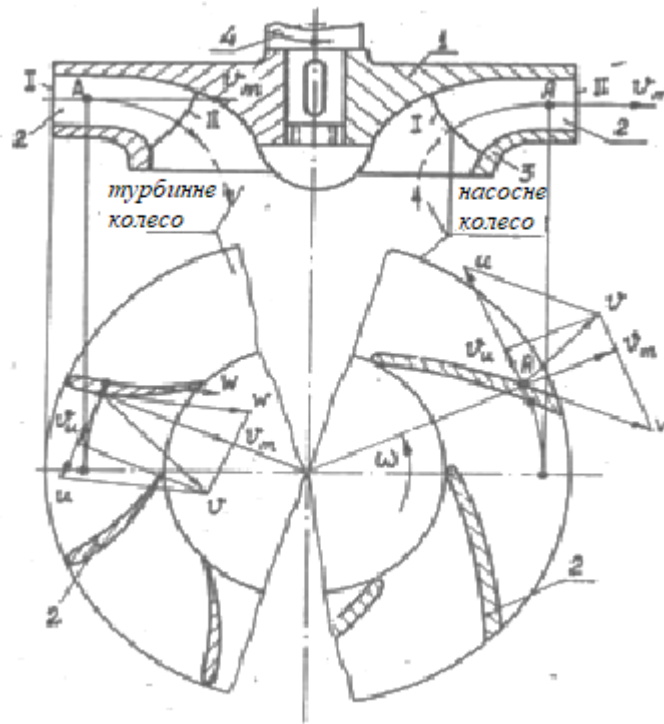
Робоче колесо лопатевої гідромашини
